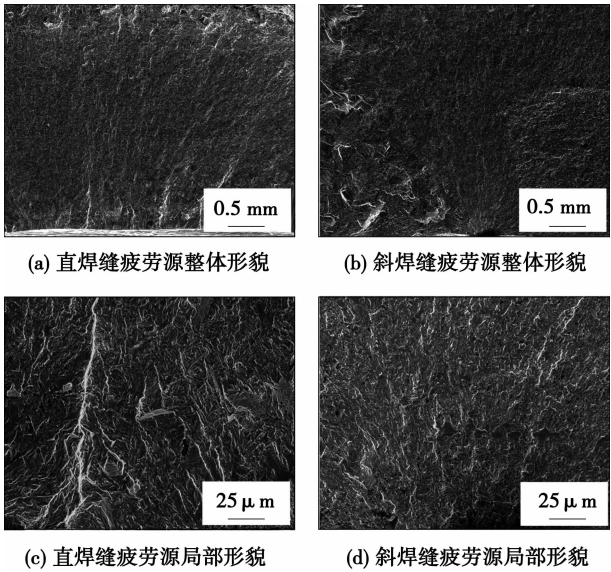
激光直、斜焊缝试件疲劳源断口形貌
